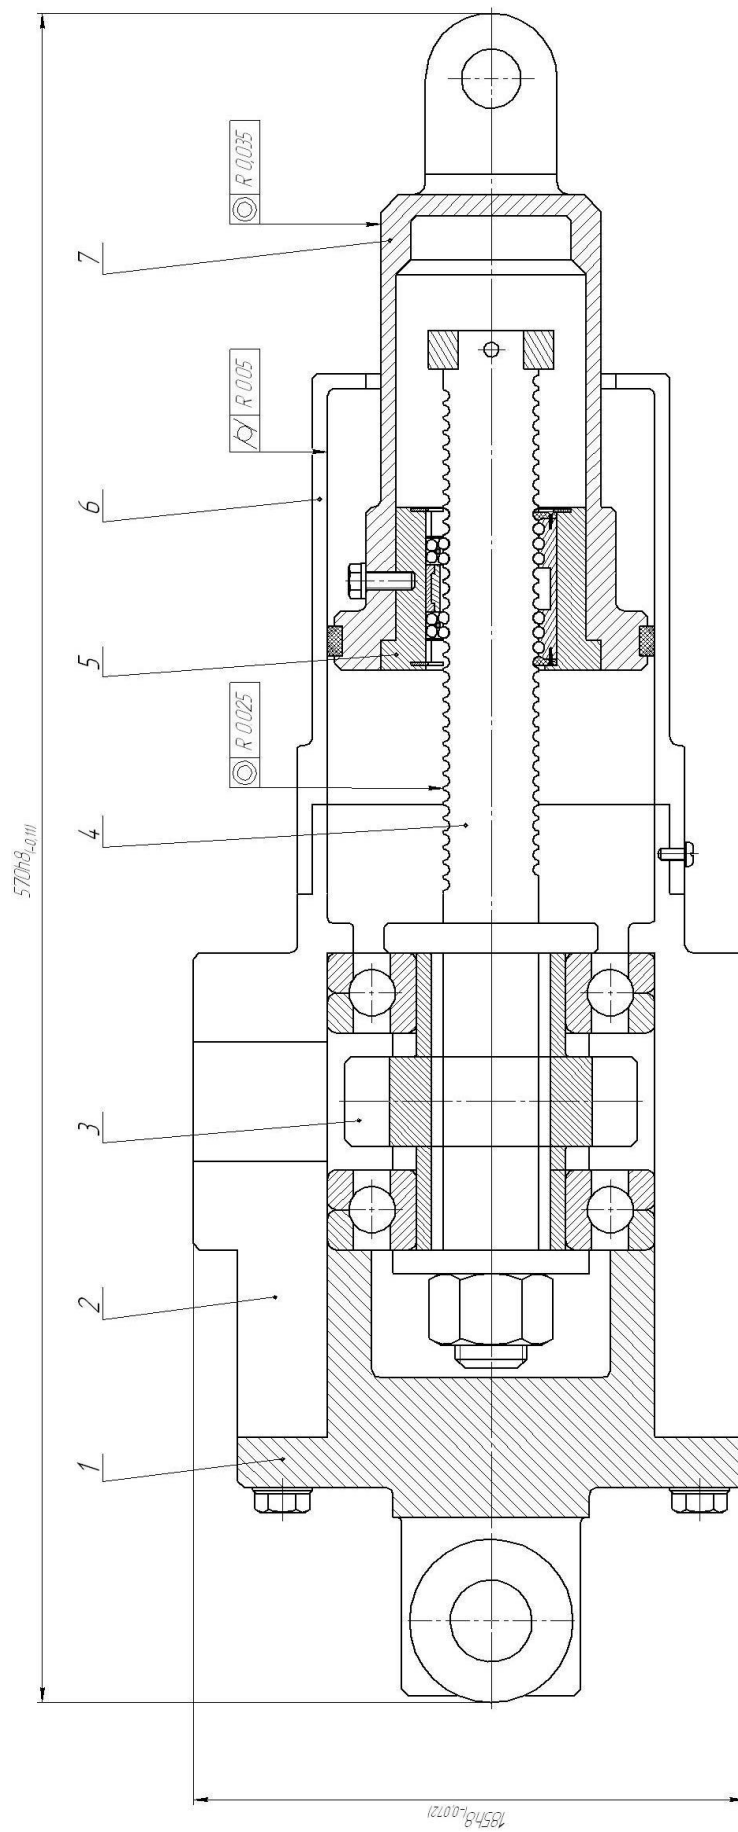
Привод линейного перемещения сварочной головки
